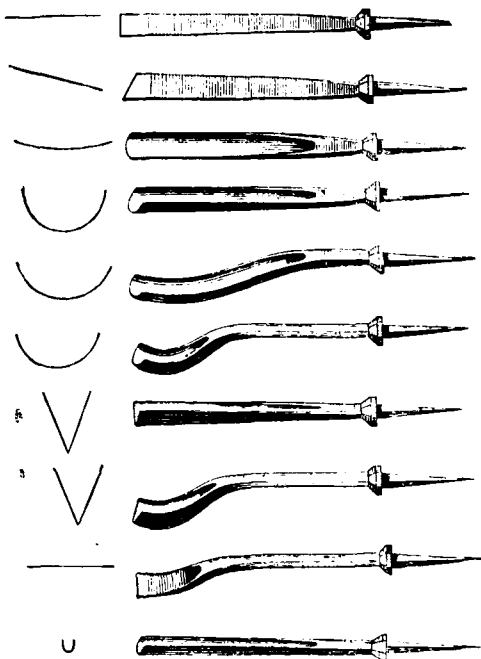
Желѣзки инструментовъ для рѣзбы по дереву.
